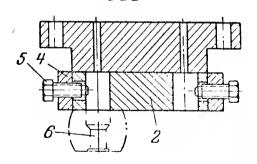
Специальный пуансонодержатель для штамповки одного или двух рядов отверстий.
